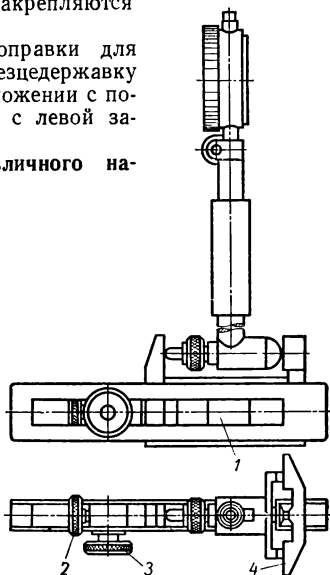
Установка нутромера на заданный размер при помощи плоскопараллельных плиток и приспособления (держателя) для них
